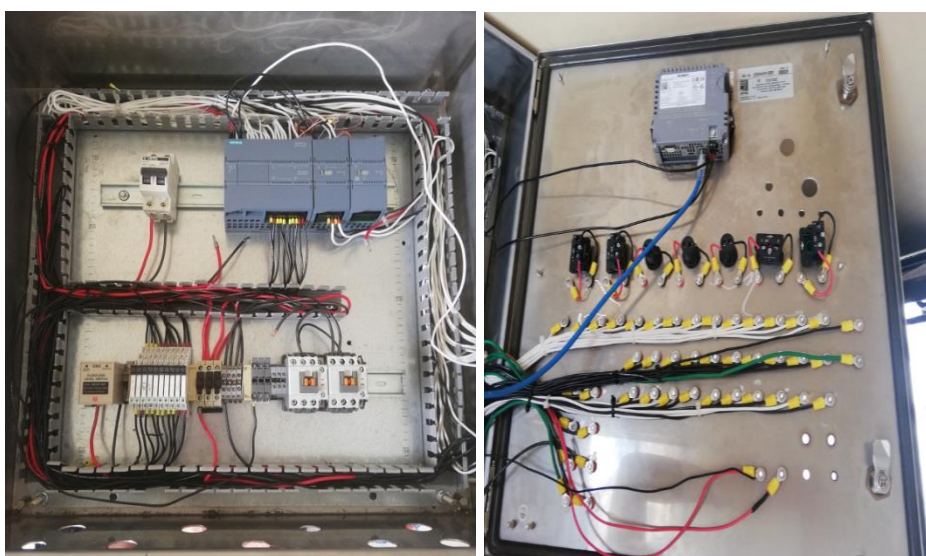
Conexionado de los dispositivos dentro del Gabinete
